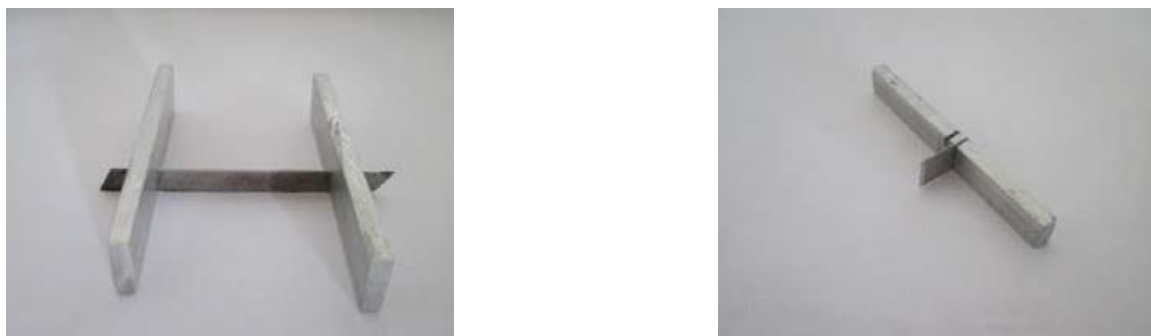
Útiles de aluminio de la serie 3: (a) útil del laminado perpendicular, (b) útil del laminado paralelo.
